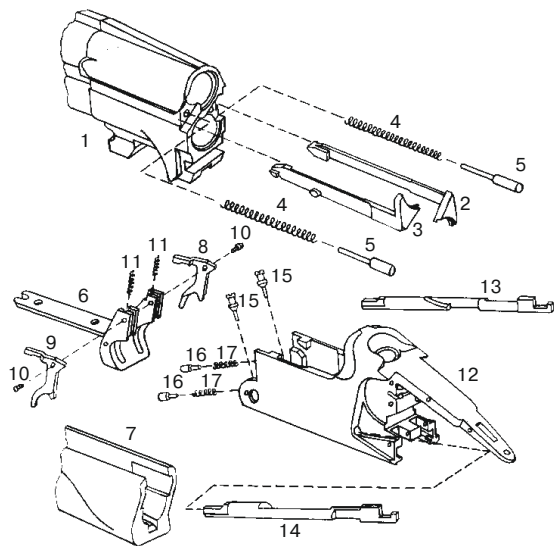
Детали ружья ИЖ-27ЕМ
